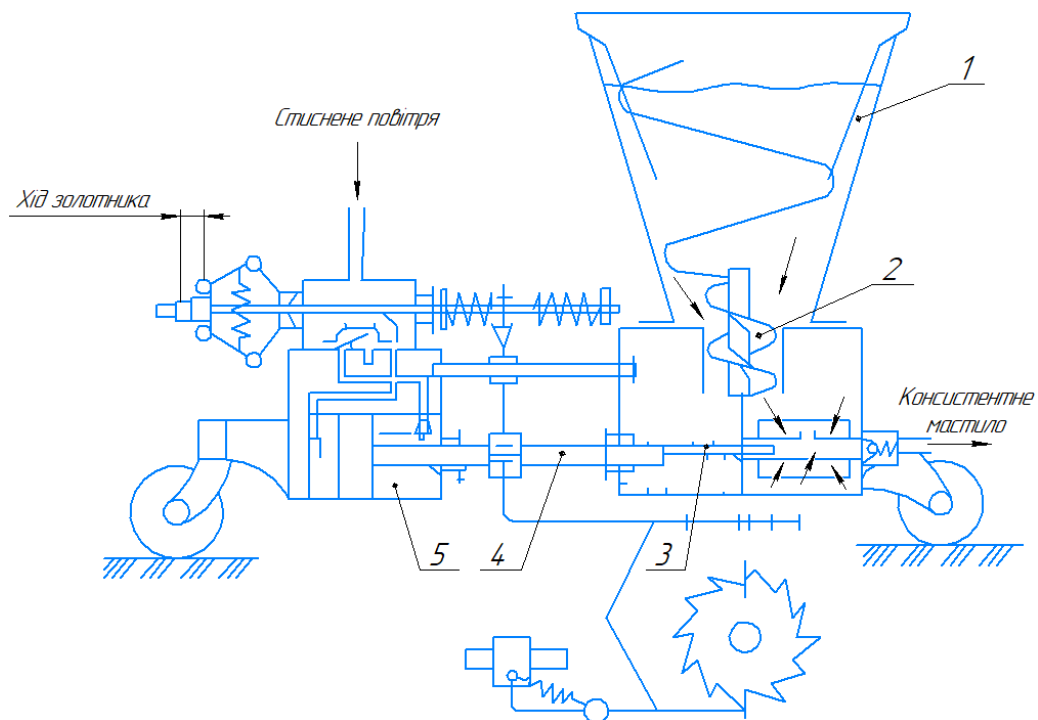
Нагнітач із пневматичним приводом: 1 – бункер; 2 – шнек з розпушувачем; 3 – плунжер насоса високого тиску; 4 – шток; 5 – поршень пневматичного двигуна.
